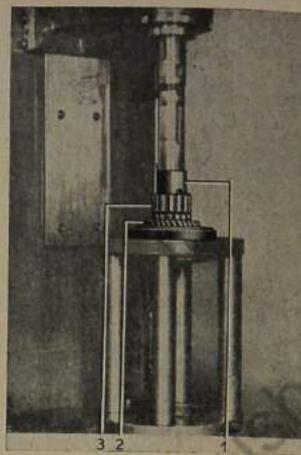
Laufbuchse zum Schrägrad für 3. Gang und Nutenkörper für 3. und 4. Gang abpressen
